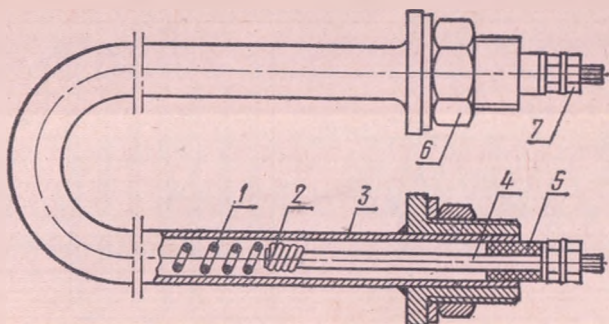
Трубчатый электронагреватель (ТЭН) герметического исполнения:
